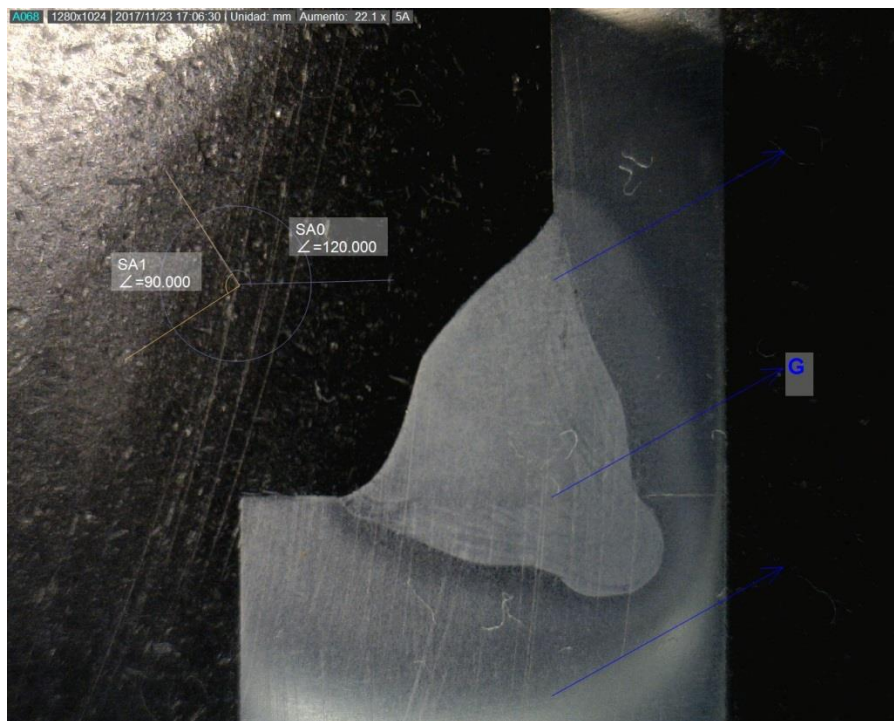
10 Perfil obtenido en cupón de soldadura 5B.
